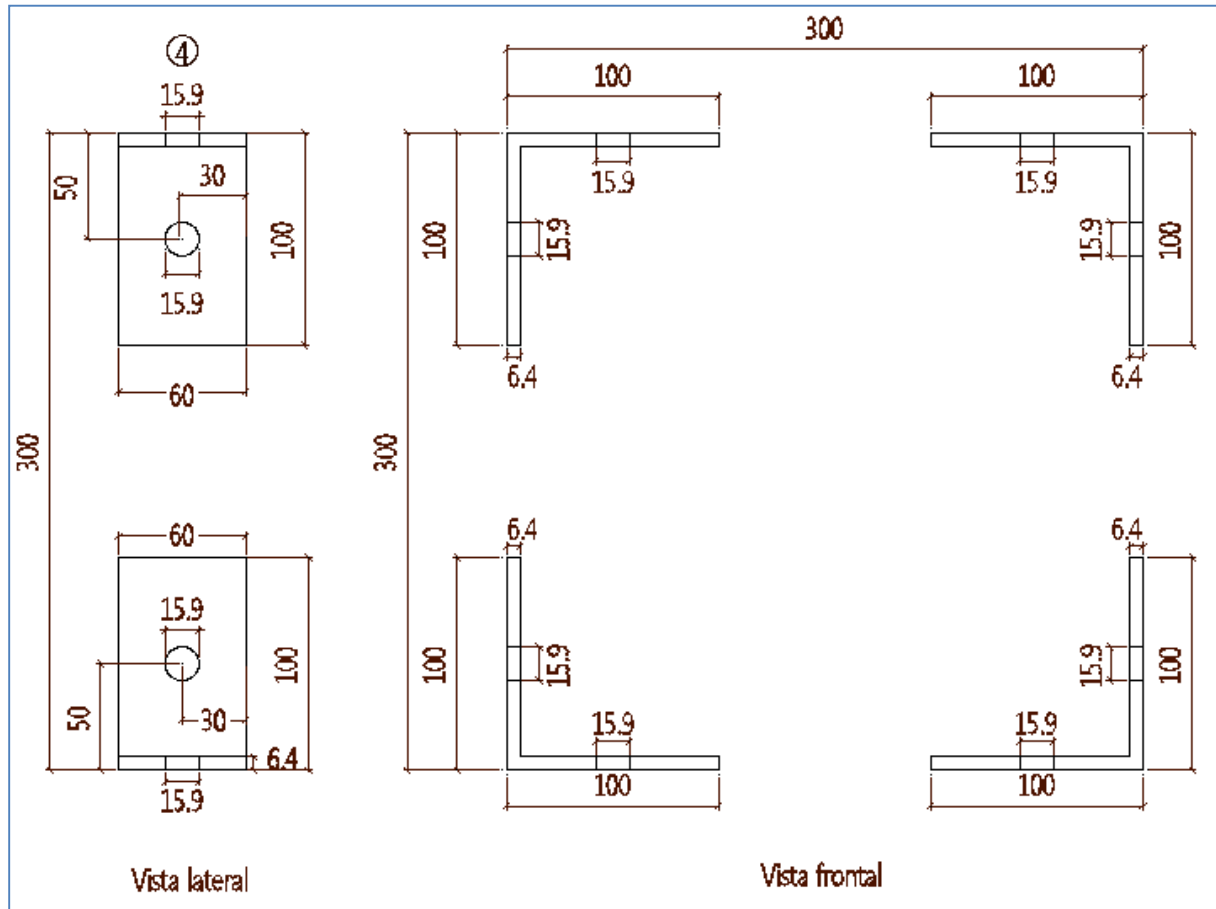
Detalle despiece pieza No.4 modelo 2 tensión.
